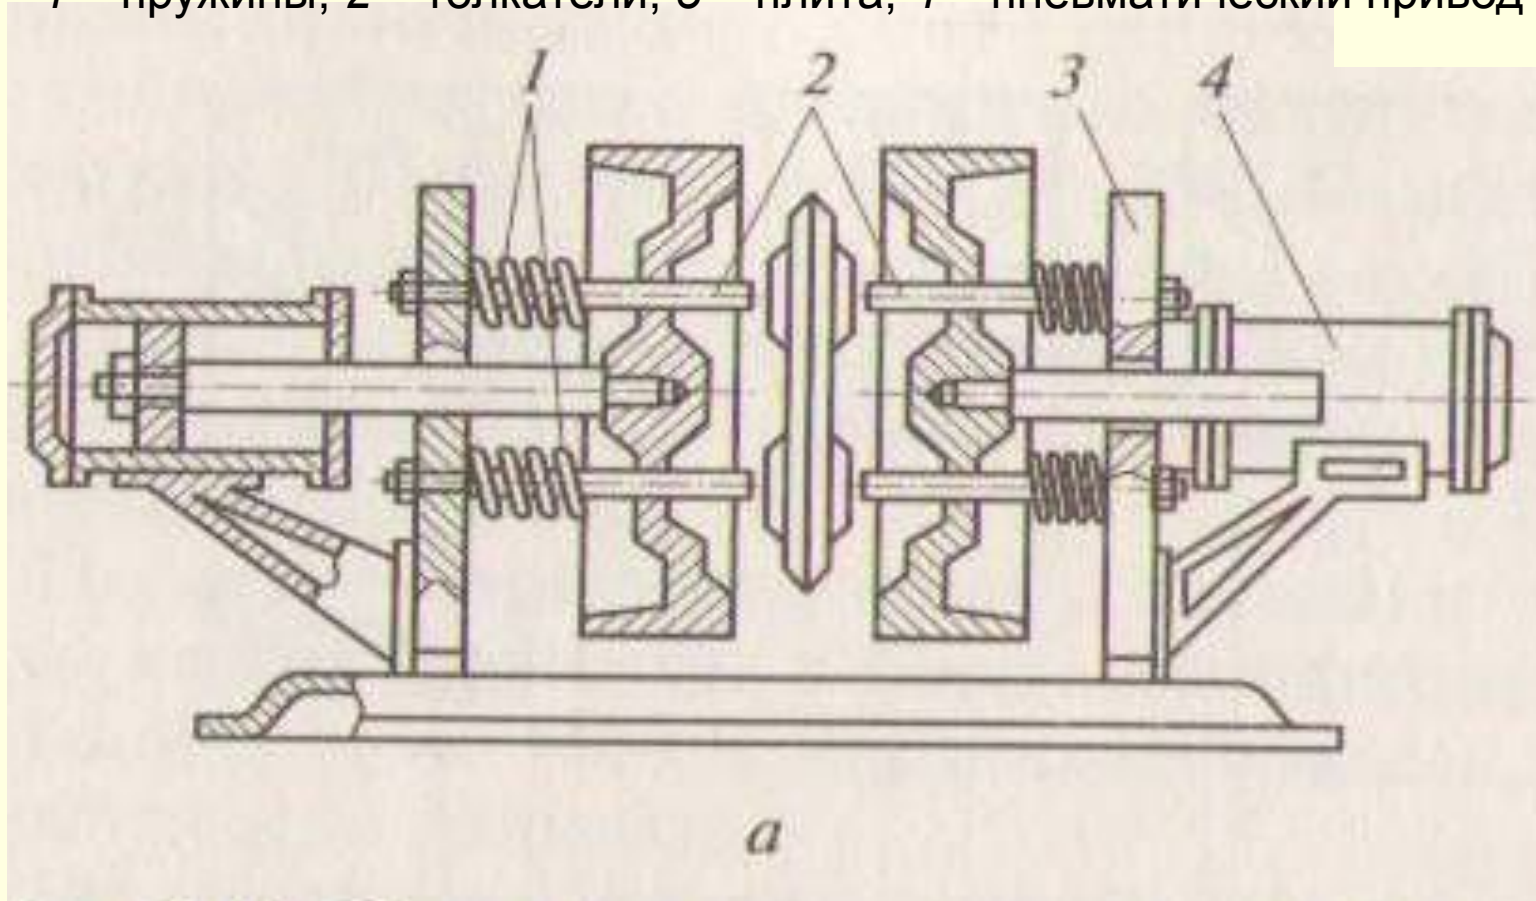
Схема кокильного станка с пневматическим приводом
